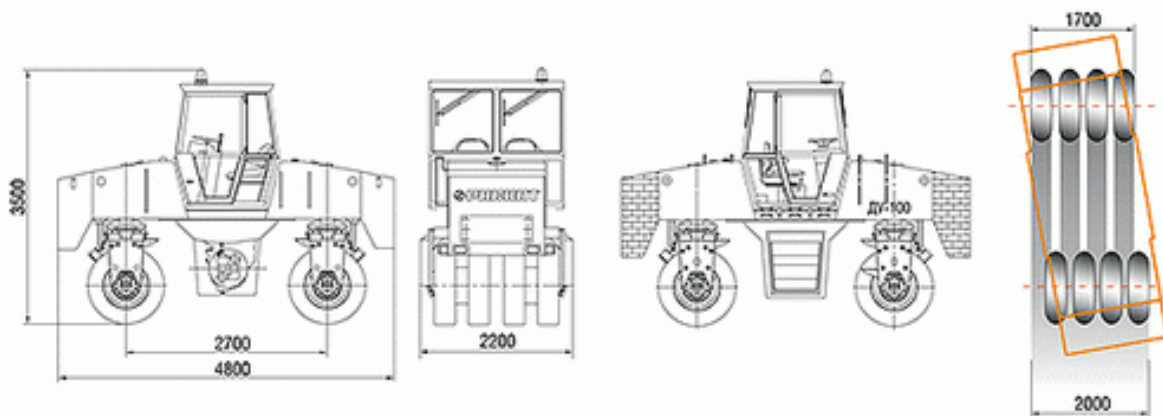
Пневмоколесний дорожній коток з робочими органами у вигляді пневматичних коліс ДУ-100
